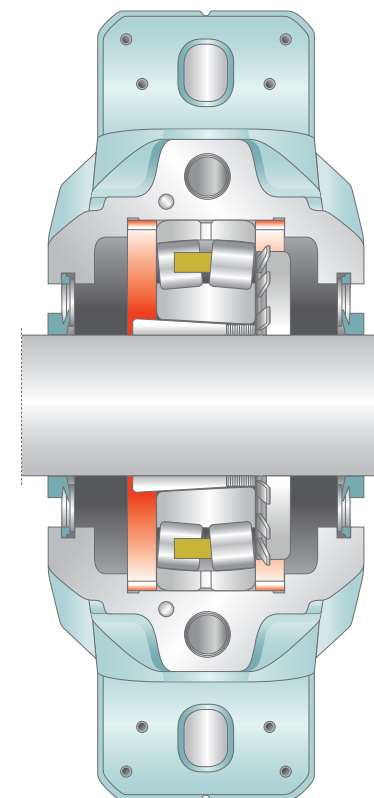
Корпус подшипника с уплотнительным кольцом FRB
